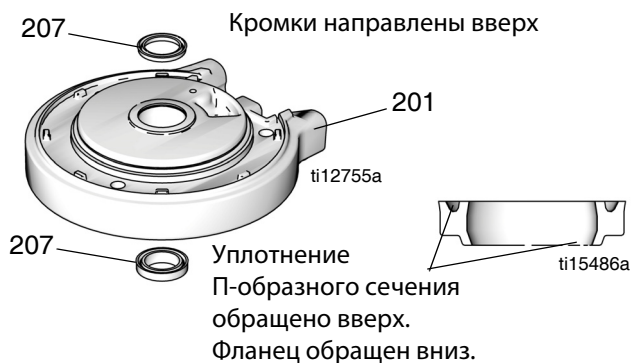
Установка уплотнение П-образного сечения в пневматический двигатель
